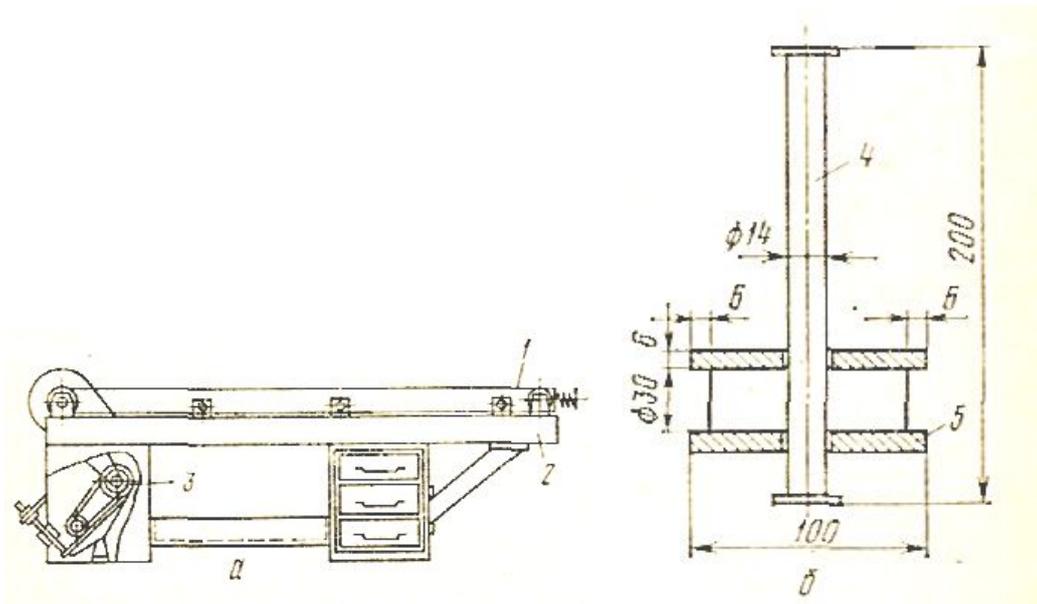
Стенд для ремонта и обкатки транспортера (а) и шаблон для установки транспортера на станке (б): 1- ремонтируемой цепной транспортер, 2- стенд, 3- привод транспортера, 4- шток, 5- направляющая шаблона.
